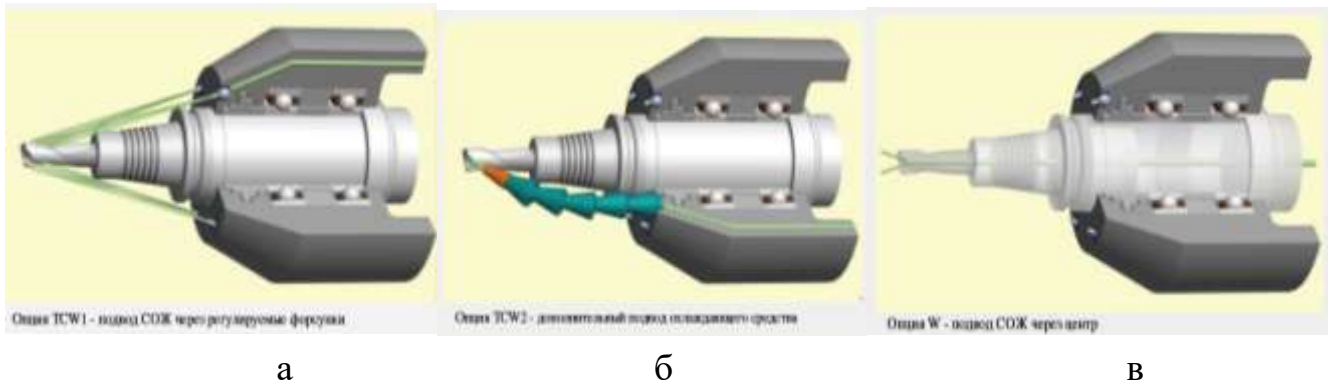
Конструктивні варіанти забезпечення охолодження інструмента та заготовки: а – через регульовані форсунки; б – через додаткову гнучку насадку; в – через центр шпинделя та інструмент [2-9].
